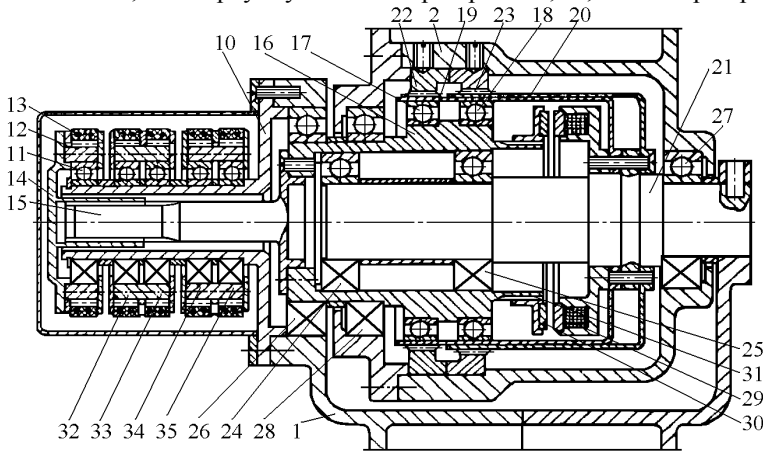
Шарнир манипулятора с двумя гибкими колесами
